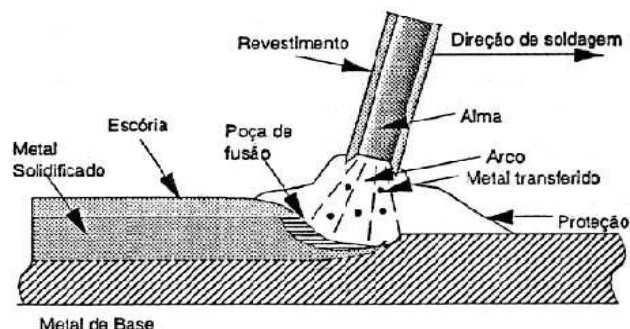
Desenho esquemático de uma soldagem com eletrodo revestido (Fonte Curso de Especialização em Soldagem, UFMG, 2015)
